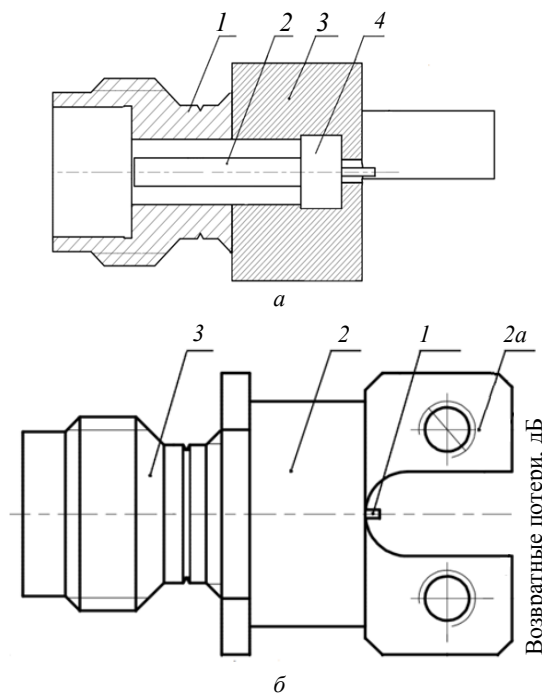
Конструктивная модель КМПП: а – боковое сечение модели, б – вид снизу. 1 – ЦП, 2 – корпус, 2а – винтовые крепления; 3 – втулка; 4 – диэлектрическая шайба
